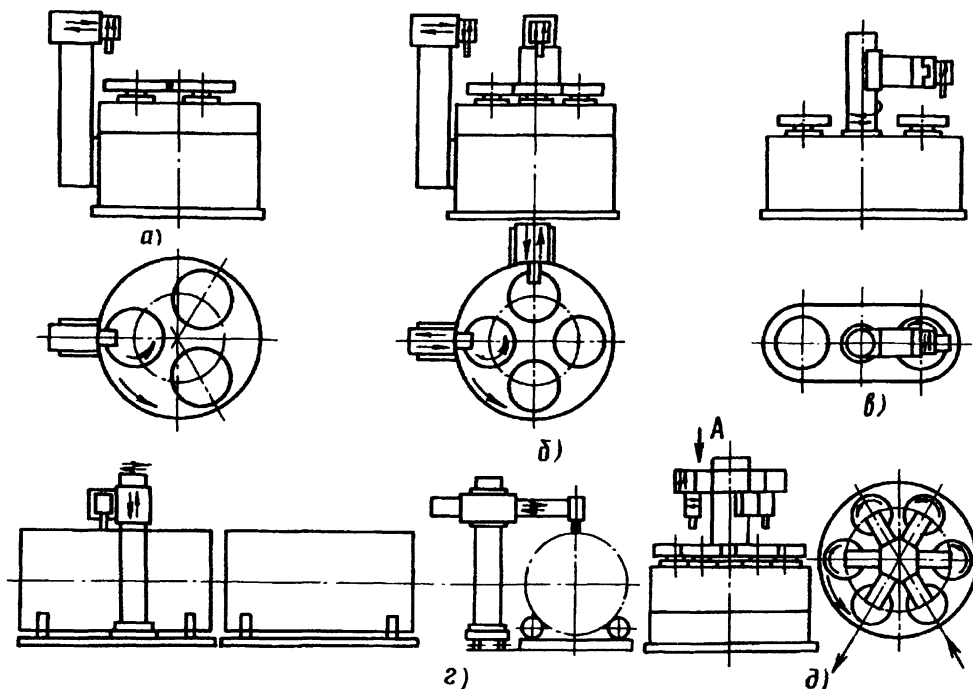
Типовые схемы компоновки многопозиционных установок и станков для дуговой сварки круговых швов
